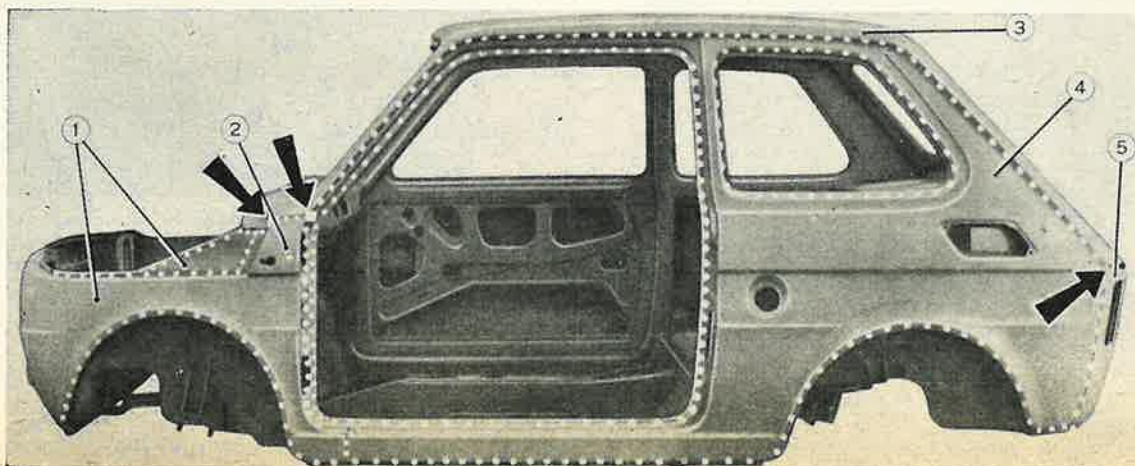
Liaisons par points de soudure des pièces composant le côté de caisse.
